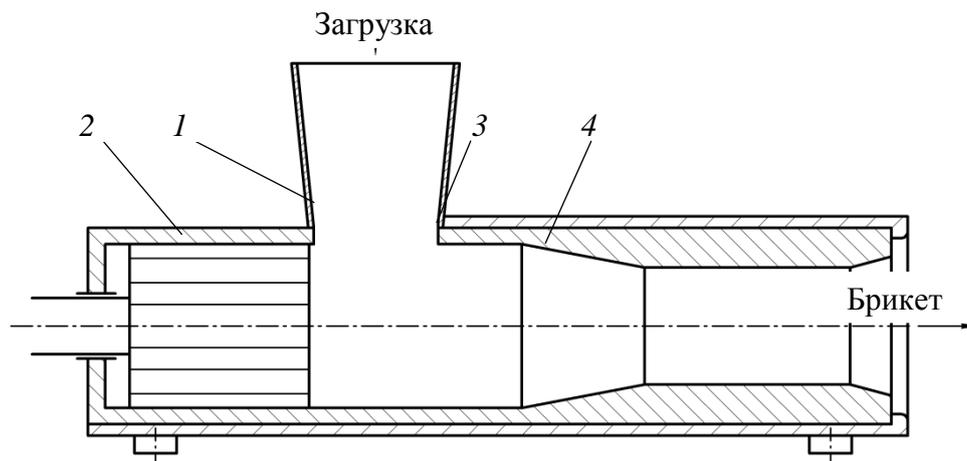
Пресс штемпельный: 1 – камера загрузочная; 2 – пуансон; 3 – корпус; 4 – матрица
